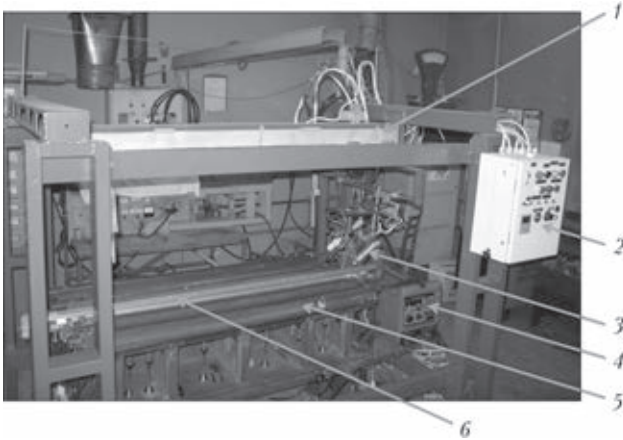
Лабораторное оборудование для аргодуговой сварки ребристых панелей в условиях ПУД: 1 — портал с тележкой для передвижения сварочной головки; 2 — блок управления; 3 — сварочная головка; 4 — источник питания; 5 — силовой сборочный стенд ПУД свариваемых деталей; 6 — сварная панель
